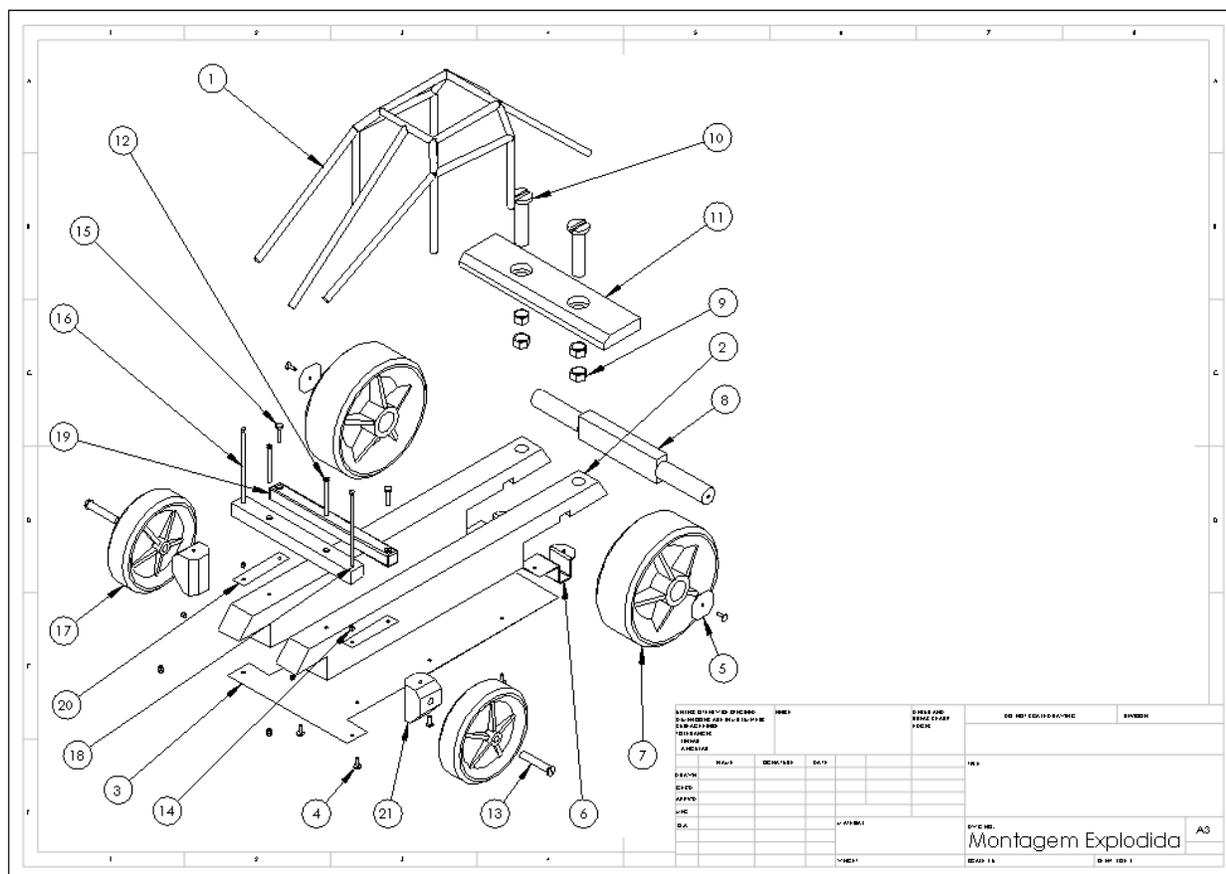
Layout do balonamento na folha do detalhamento.
